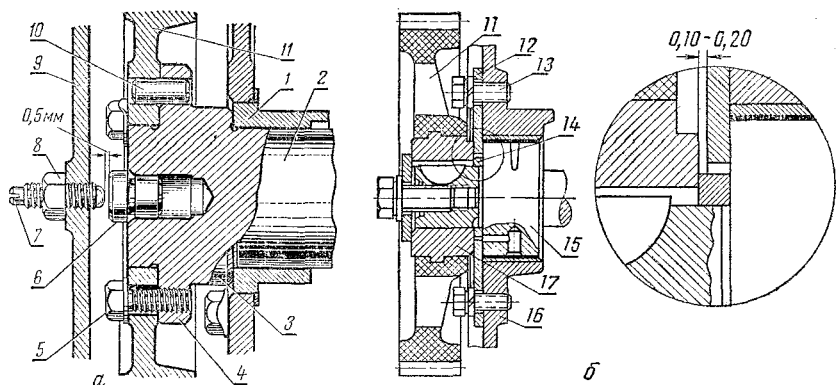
Устройство, ограничивающее осевое перемещение распределительного вала: а — двигателя СМД-14; б — двигателя ГАЗ-52-01; 1 — передняя втулка распределительного вала; 2 — распределительный вал; 3 — упорный бурт распределительного вала; 4 — фланец; 5, 13 — болты; 6 — подпятник упорного винта; 7 — упорный винт; 8 — контргайка; 9 — крышка картера шестерен; 10 — установочный штифт; 11 — шестерня распределительного вала; 12 — упорная шайба; 14 — распорное кольцо; 15 — опорная шейка распределительного вала; 16 — блок-картер; 17 — ступица распределительной шестерни.
